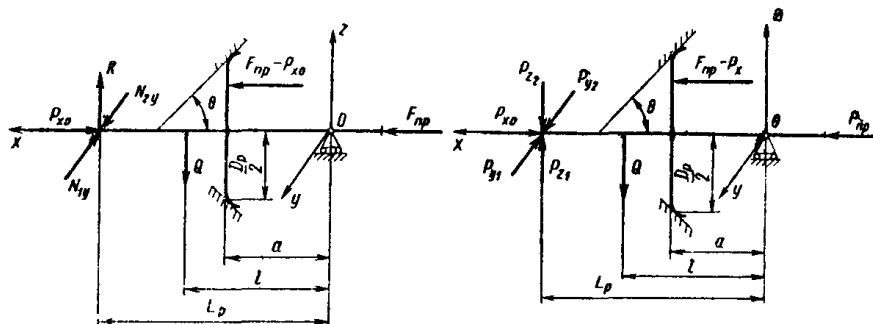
Схема дії сил в дволезовій розвертці, що коливається, для багатошпindelних автоматів
